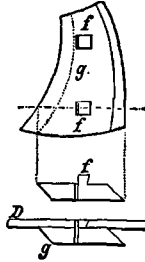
Dies ou pièces composant la meule dormante de la chaudière Wheeler.
